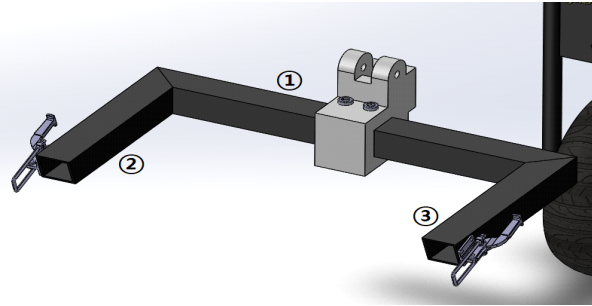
'ㄷ' shape structure and wheelchair connecting part
